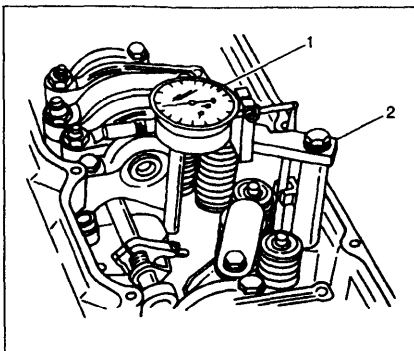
Приспособление для регулировки форсунки в установленном положении:
